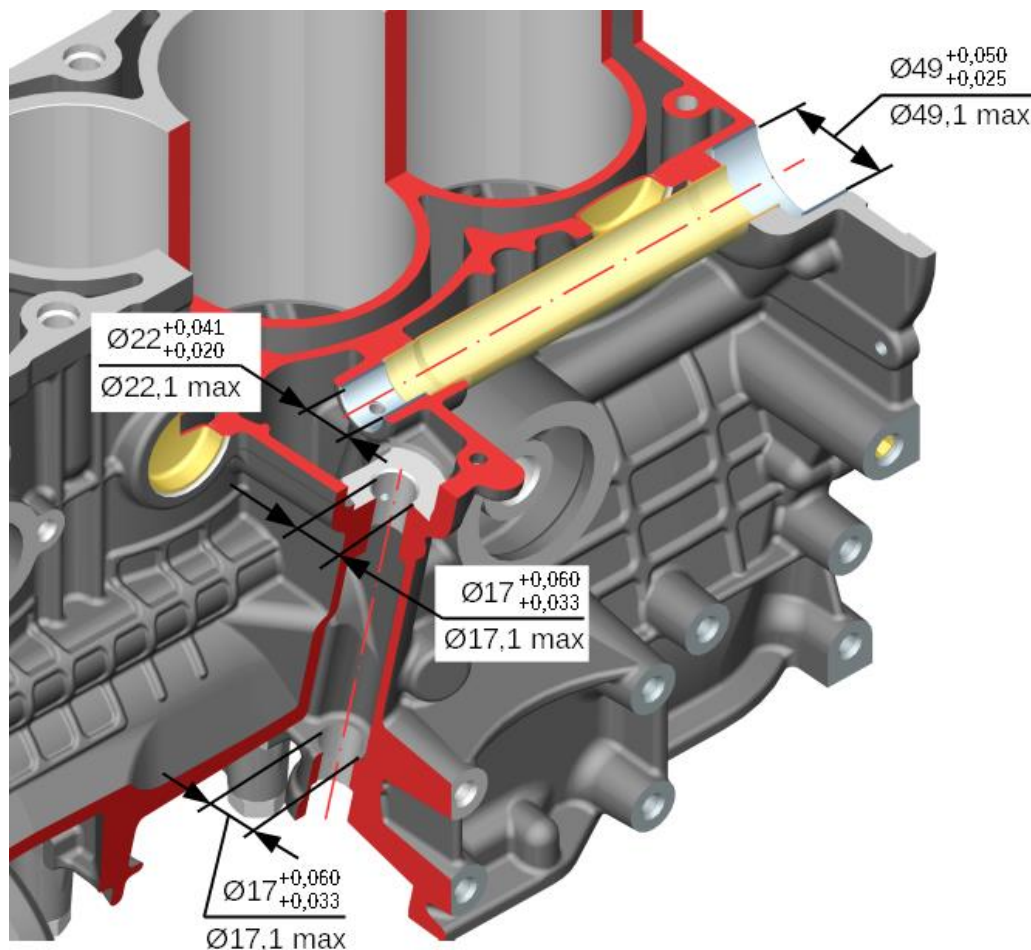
Номинальные и предельные размеры опор промежуточного вала и опор привода масляного насоса
